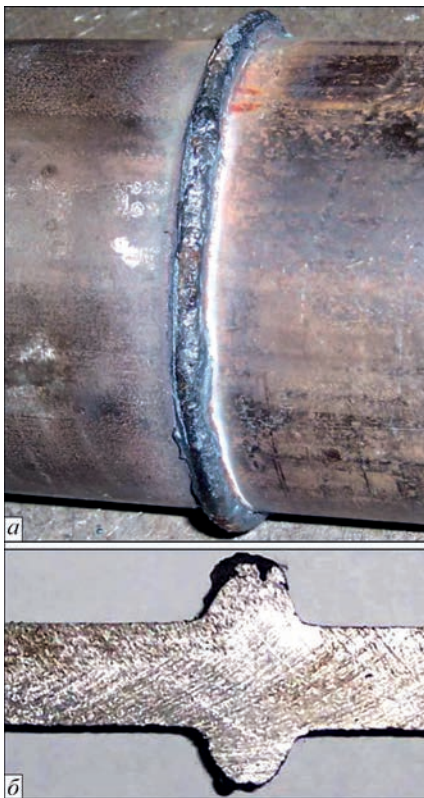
Формування зварного з'єднання труб без припуску на осадку: *а* – загальний вигляд зварного з'єднання; *б* – поперечний переріз зварного з'єднання
